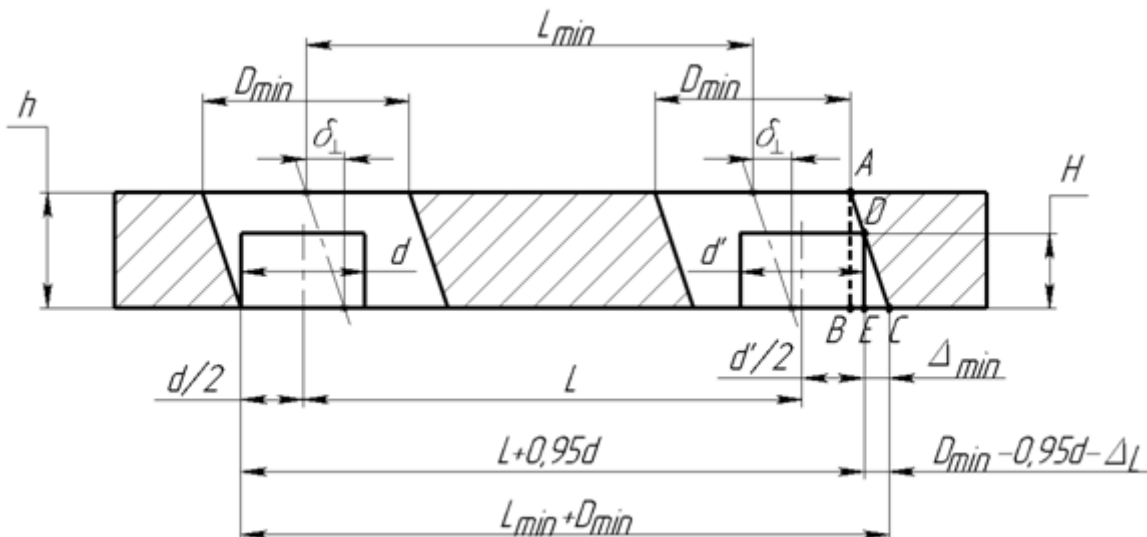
Схема установки заготовки на два пальці при неперпендикулярності базових отворів базовій площині
